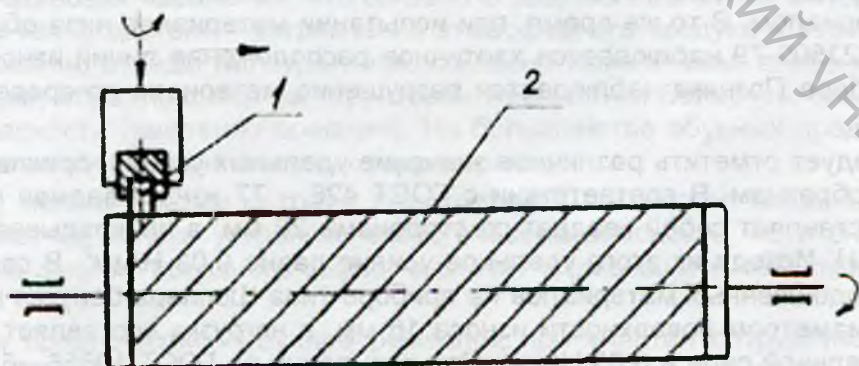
Кинематическая схема прибора для испытаний по закрепленному абразиву по возобновляемой поверхности:
